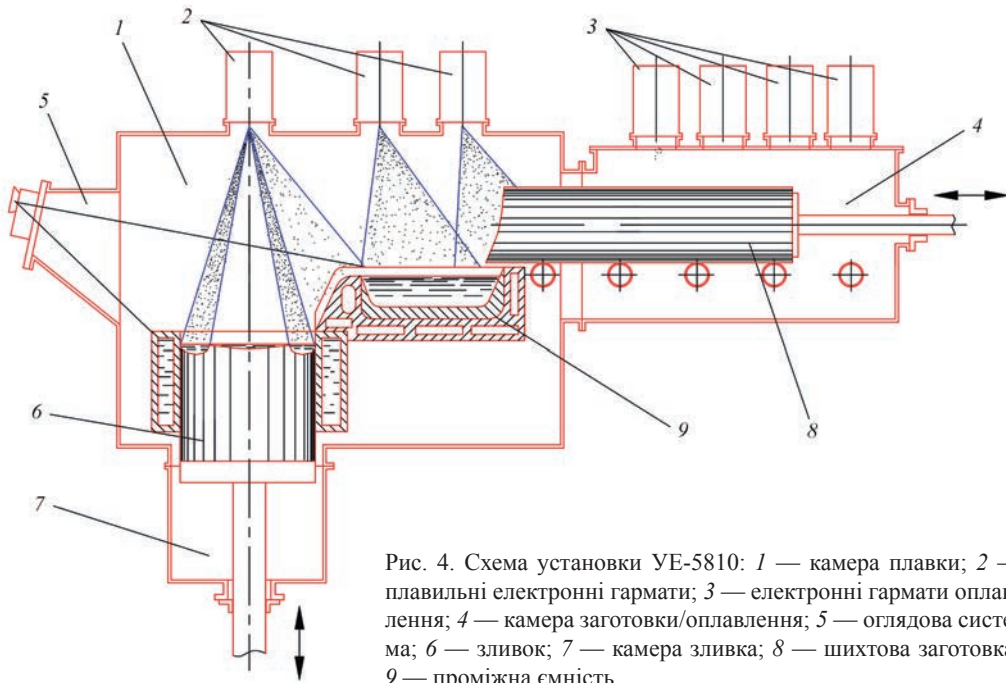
Схема установки UE-5810: 1 — камера плавки; 2 — плавильні електронні гармати; 3 — електронні гармати оплавлення; 4 — камера заготовки/оплавлення; 5 — оглядова система; 6 — зливок; 7 — камера зливка; 8 — шихтова заготовка; 9 — проміжна ємність
